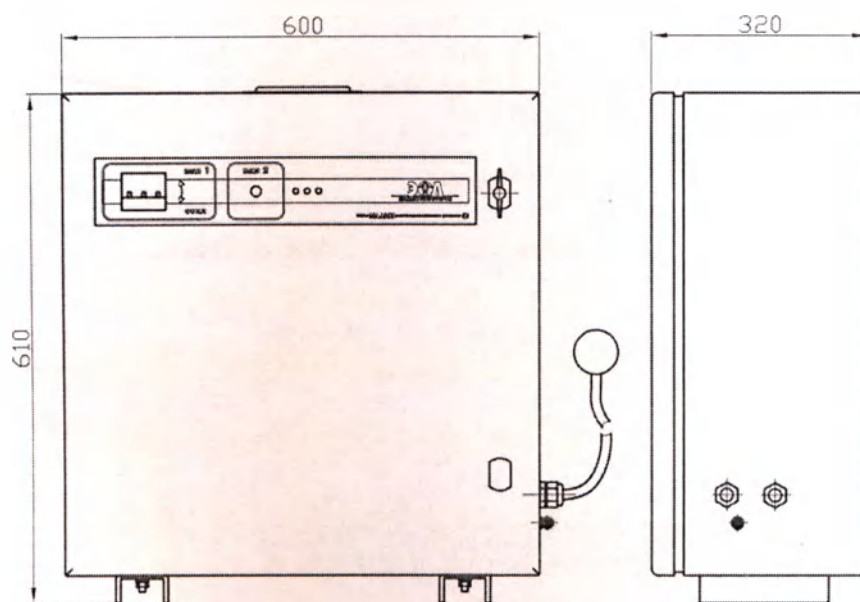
Габаритные размеры блока выпрямителя установки исполнения Стандарт
